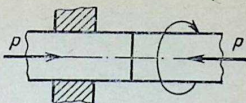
Принципиальная схема процесса сварки трением.
